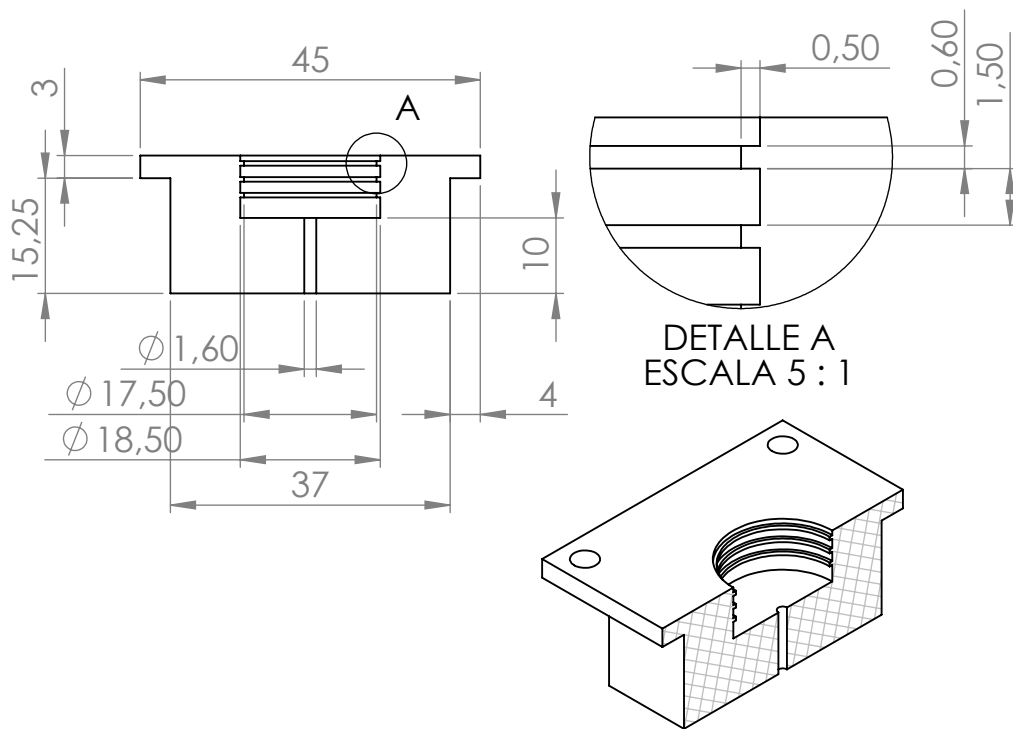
Vista en corte del molde del *Robot Uniaxial* parte A
